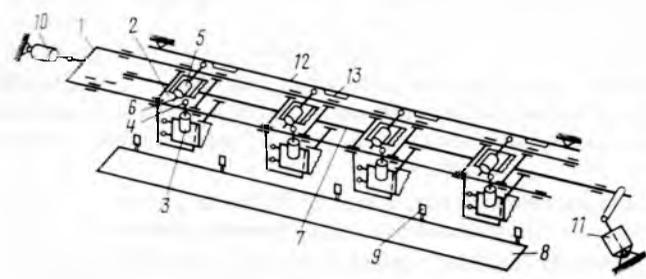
Схема фрезерного полуавтомата для обработки оконных створок
